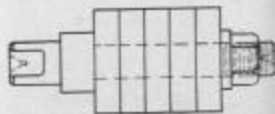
Mandrin à écrou pour Finition de Galets d'Engrenages
